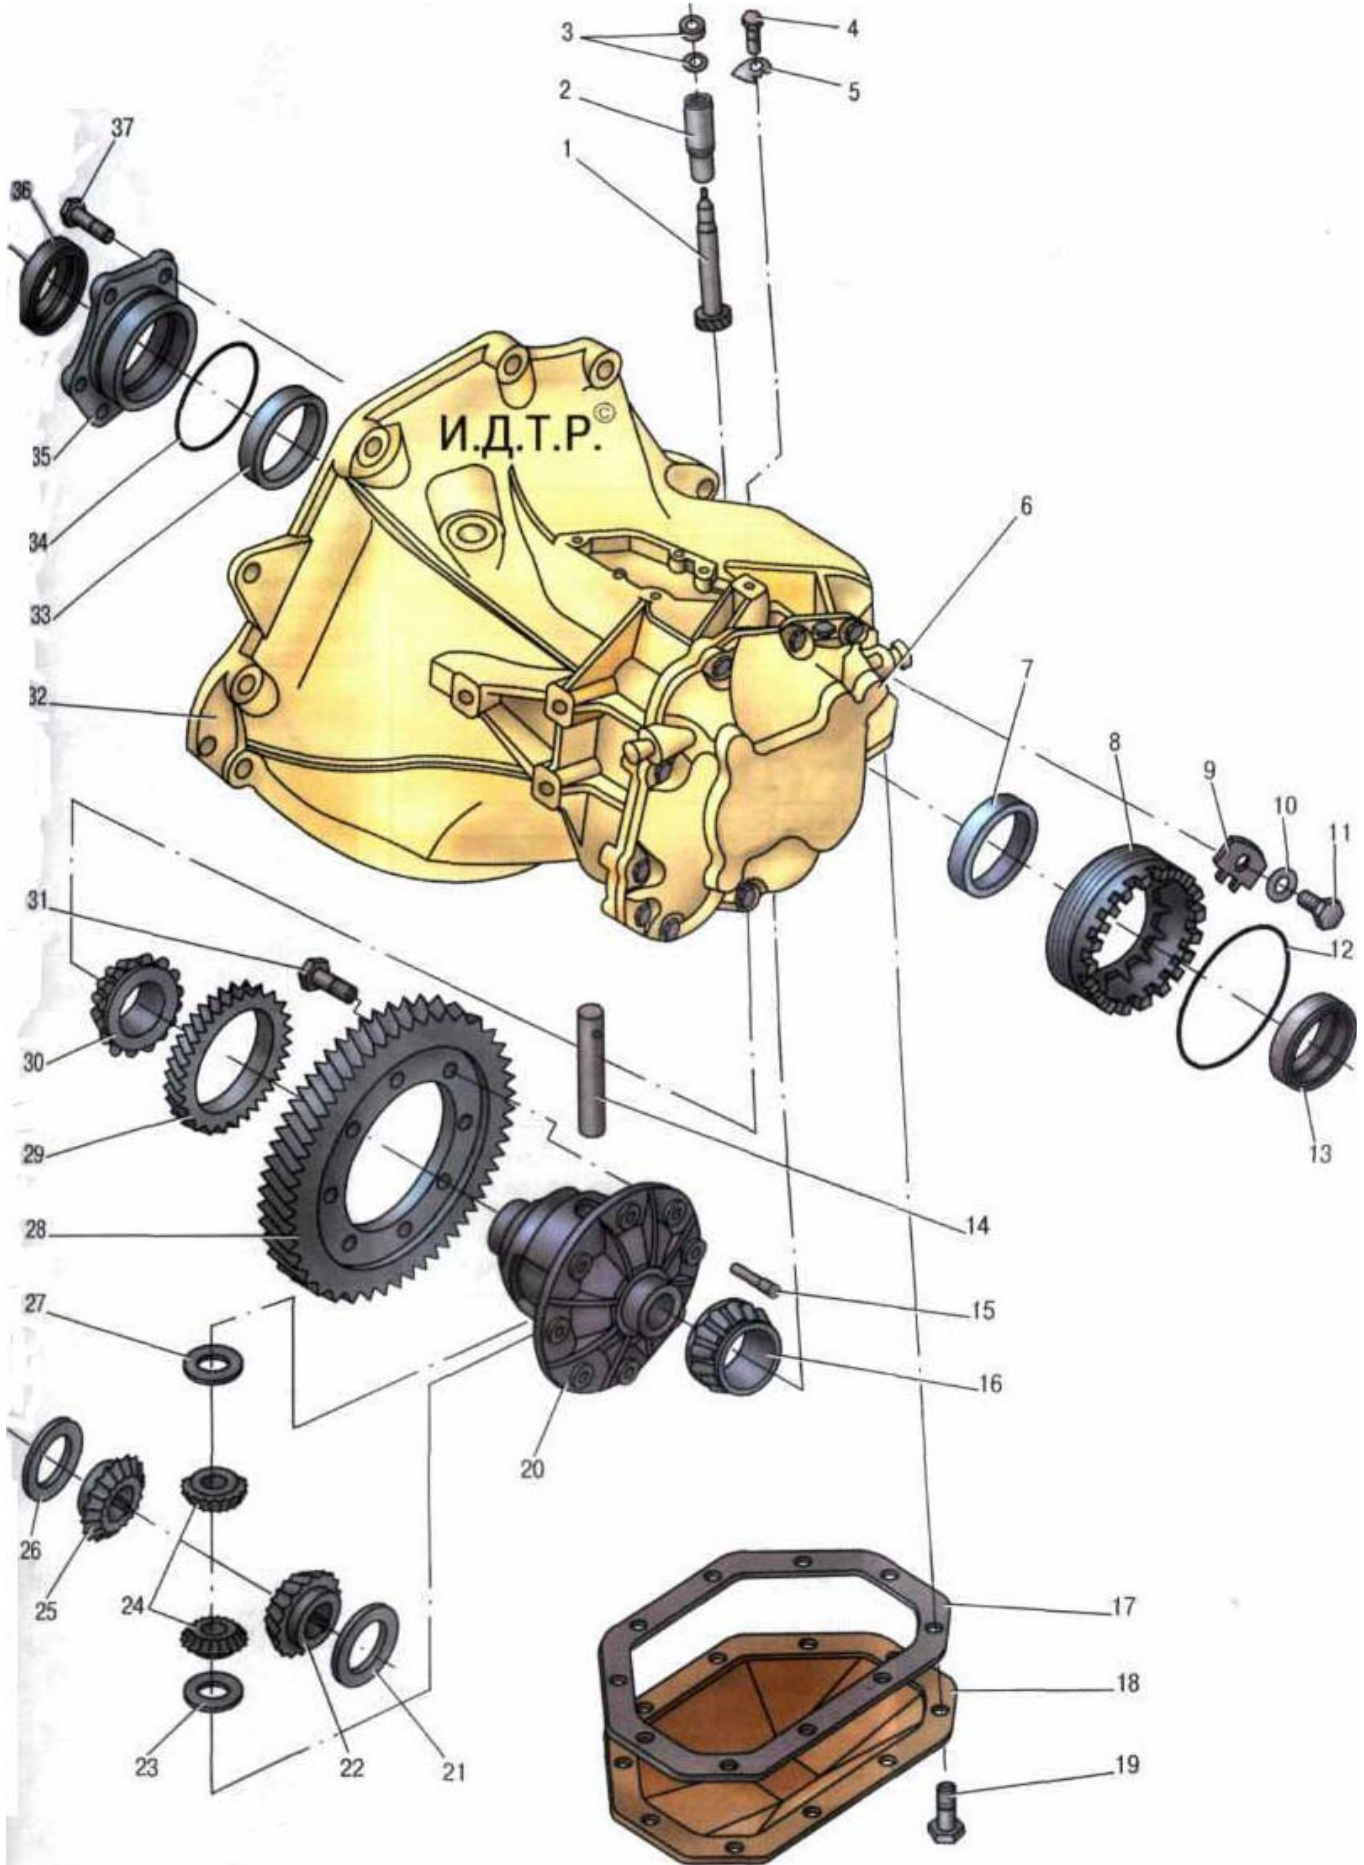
Главная передача и дифференциал: 1 - вал-шестерня редуктора привода спидометра; 2 - корпус редуктора привода спидометра; 3, 12, 34 - уплотнительные кольца; 4, 11, 19, 31, 37 - болты; 5 - стопорная пластина; 6 - крышка коробки передач; 7, 33 - наружные кольца подшипников дифференциала; 7 - регулировочная гайка подшипников; 9 - пластина фиксатора; 10 - шайба; 13, 36 - сальники; 14 - ось сателлитов дифференциала; 15 - фиксатор оси сателлитов; 16, 30 - конические роликовые подшипники дифференциала; 17 - прокладка; 18 - нижняя крышка; 20 - корпус дифференциала; 21, 26 - упорные шайбы; 22, 25 - полуосевые шестерни; 23, 27 - упорные шайбы сателлитов; 24 - сателлиты; 28 - ведомая шестерня главной передачи; 29 - ведущая шестерня привода спидометра; 32 - картер коробки передач; 35 - правая крышка подшипников дифференциала.
